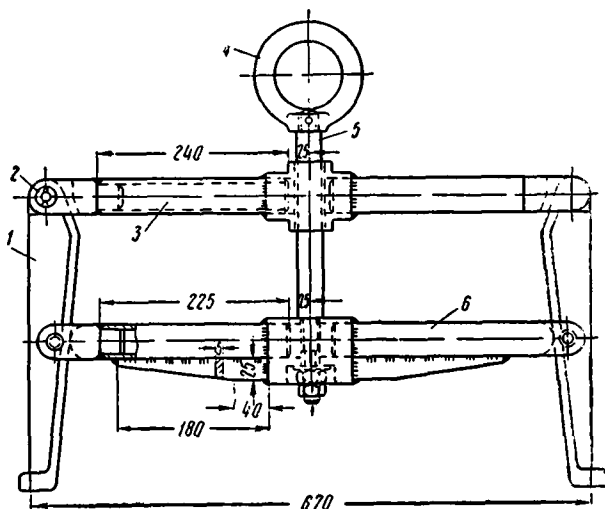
Приспособление для подъема и установки траверсы в остов двигателя НБ-412М:
